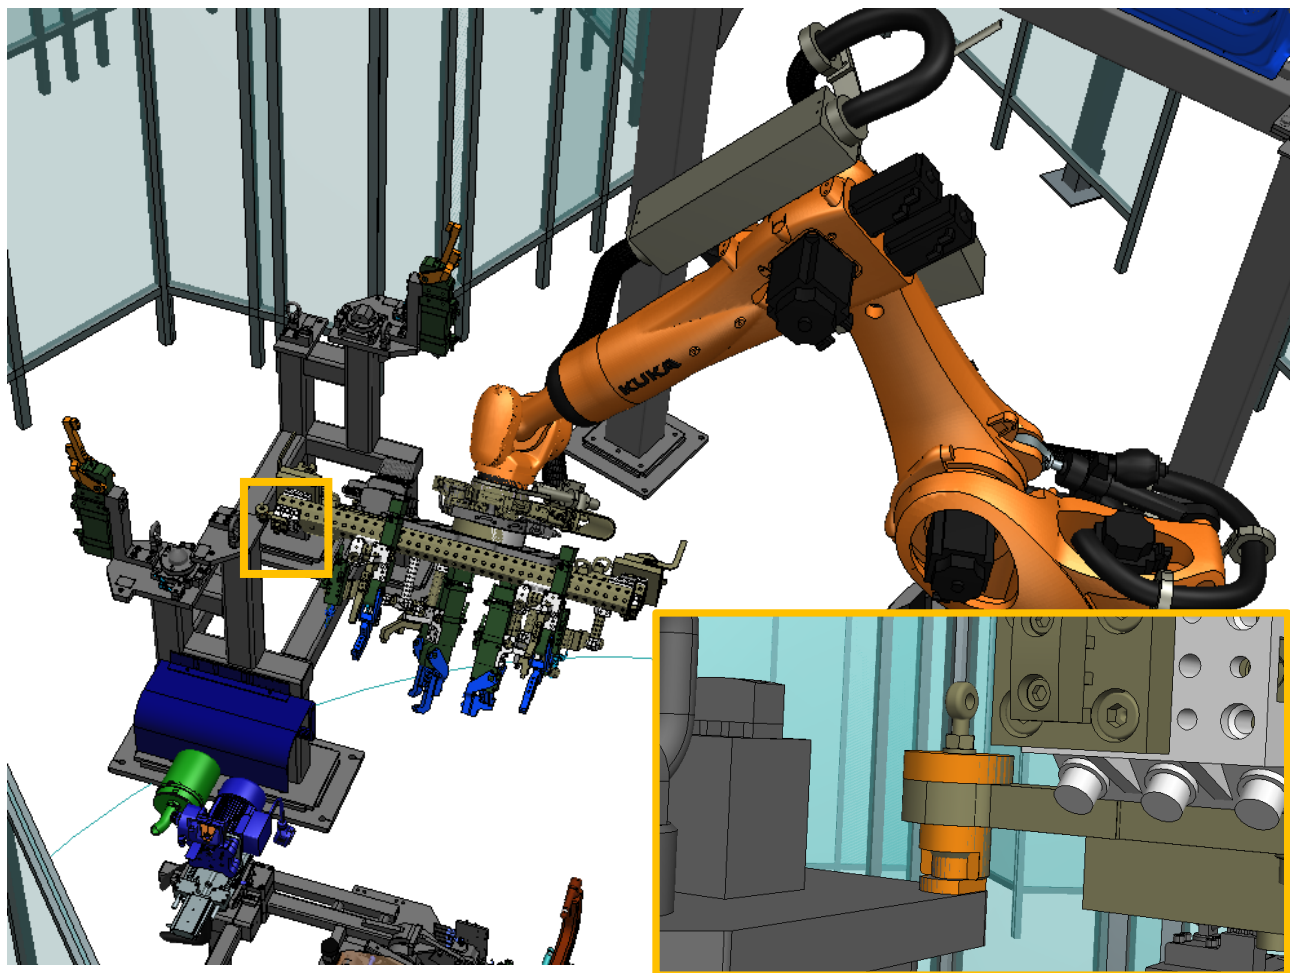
Положение робота в позиции калибровки захватного устройства
